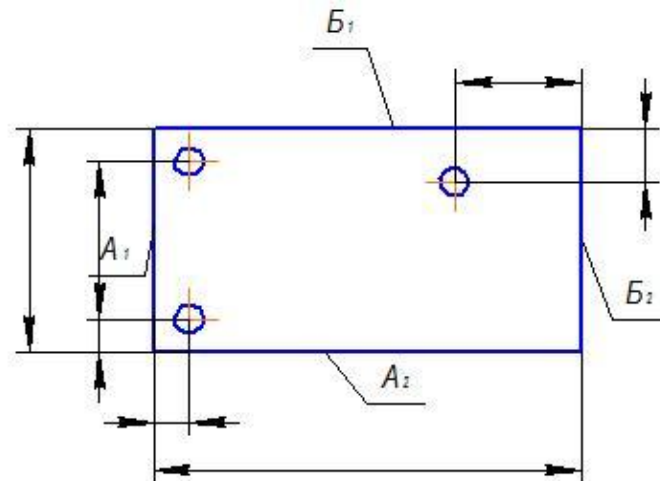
Негативний приклад вказування розмірів від двох конструктивних баз
